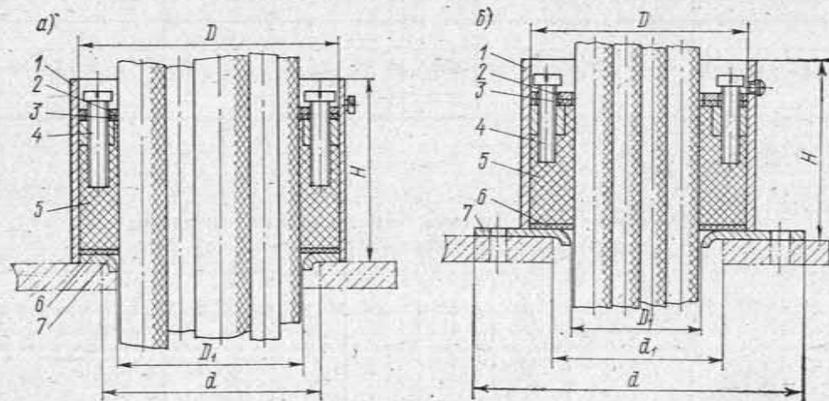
Патрубки уплотнительные для групп кабелей: а — типа I; б — типа II. 1 — корпус; 2 — кольцо; 3, 6 — шайбы; 4 — нажимные винты; 5 — уплотнительный материал; 7 — фланец.
